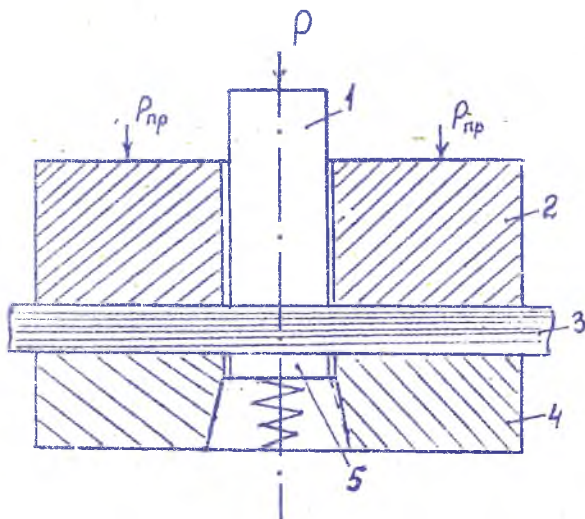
Схема динамической пробивки в инструментальном штампе: 1 – пуансон; 2 – направляющая плита; 3 – обрабатываемая заготовка; 4 – матрица; 5 – подпор
